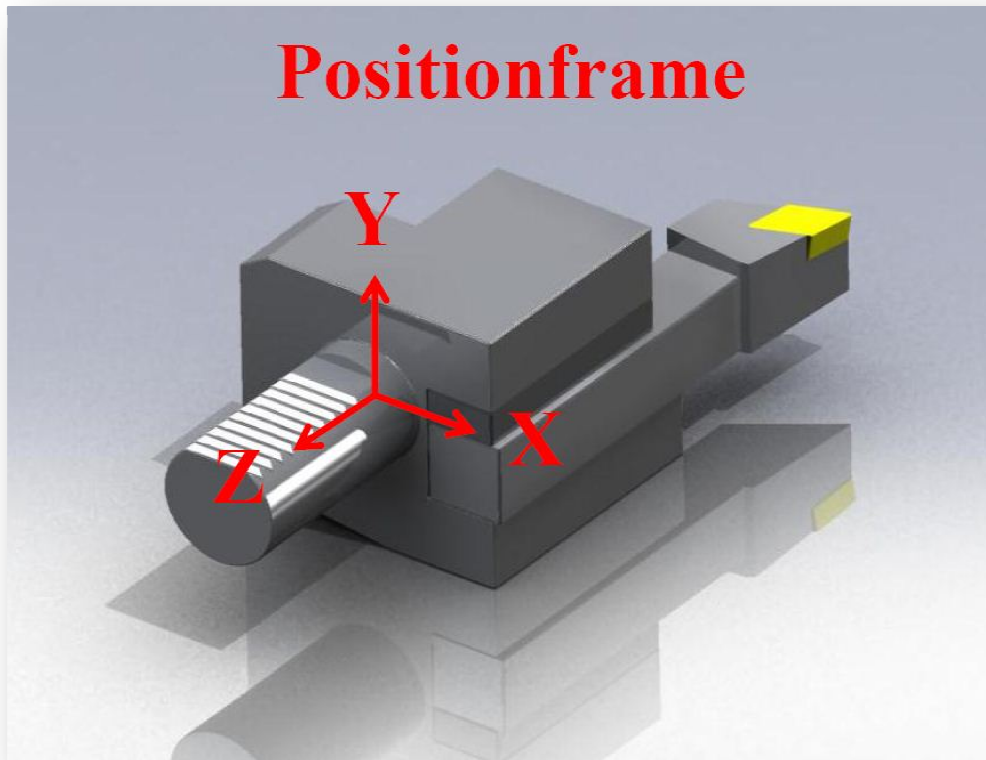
Lage des Positionframe der Werkzeugaufnahme
